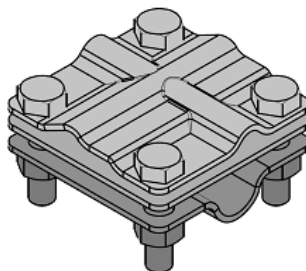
Conector atornillado, diseñado para el cruce de cables.
